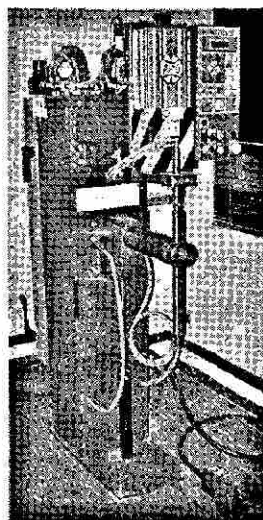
Máquina soldadora de pedestal utilizada para la prueba de soldadura localizada en la empresa Galvak, S.A de C.V.
